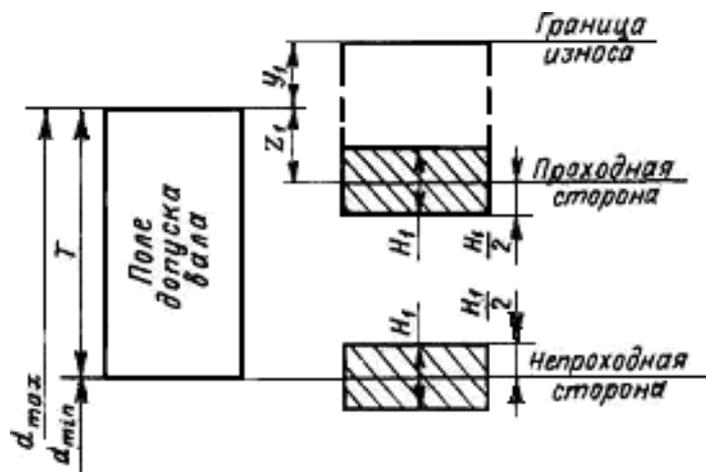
Схема расположения полей допусков калибров для валов
